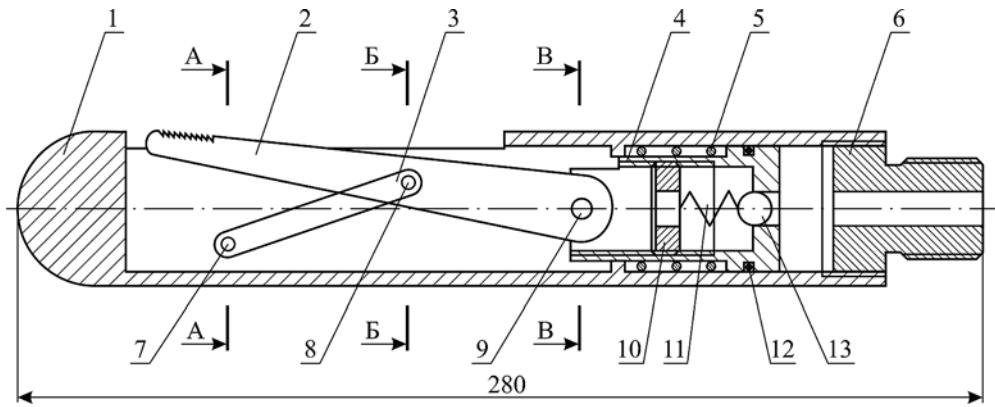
Схема щелеобразователя гидравлического по углю (ЩГУ): 1 – корпус; 2 – режущий орган; 3 – кронштейн; 4 – поршень; 5 – пружина возврата; 6 – переходник; 7, 8, 9 – оси крепления; 10 – опорная регулирующая гайка; 11 – пружина; 12 – уплотнение; 13 – шарик
